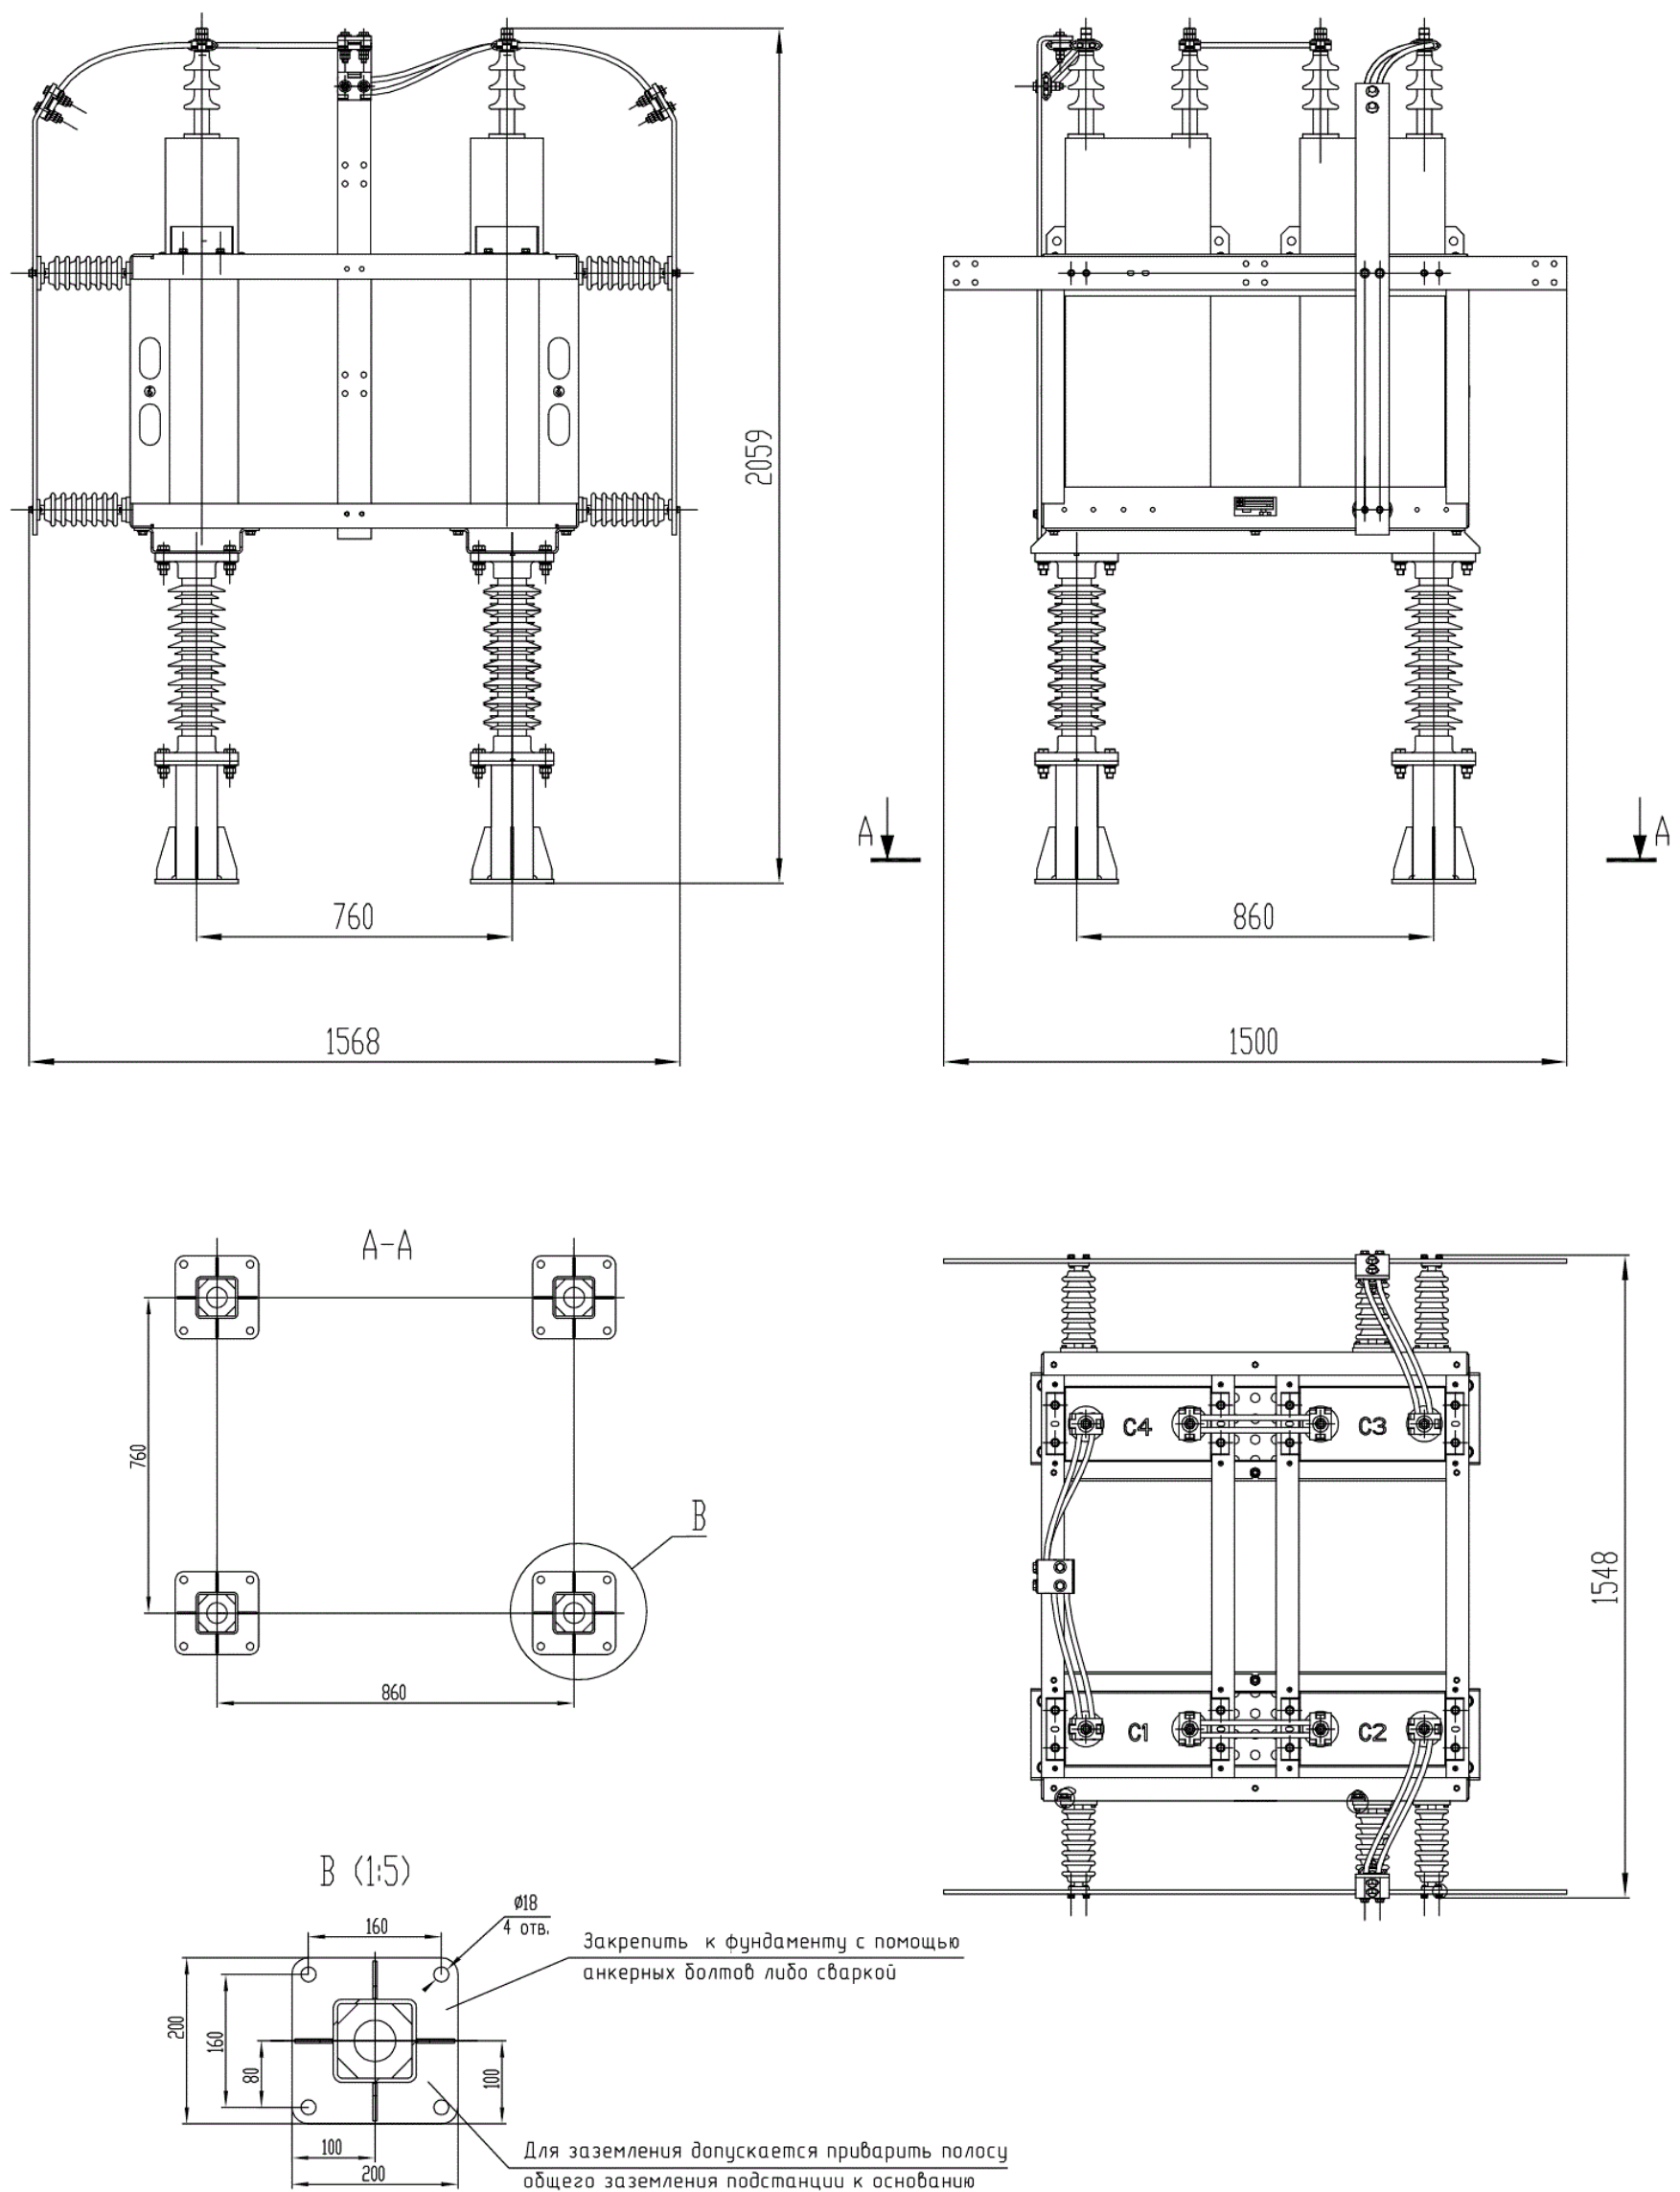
Габаритный чертеж батареи конденсаторной
